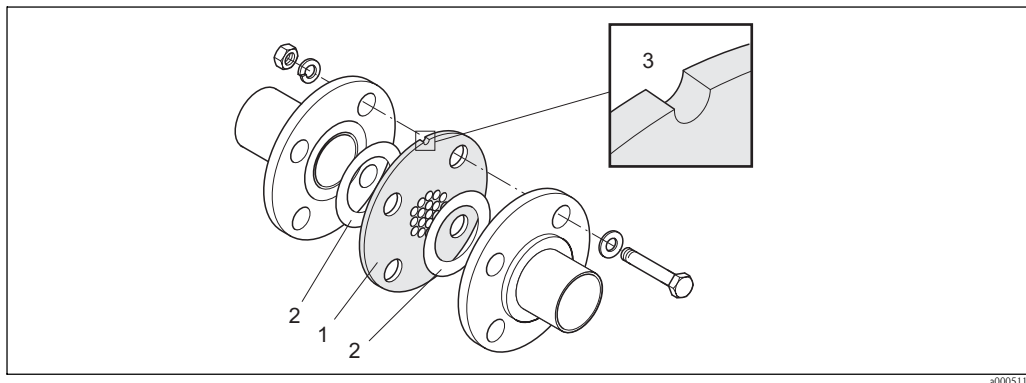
Montaje del acondicionador de caudal (ejemplo)
